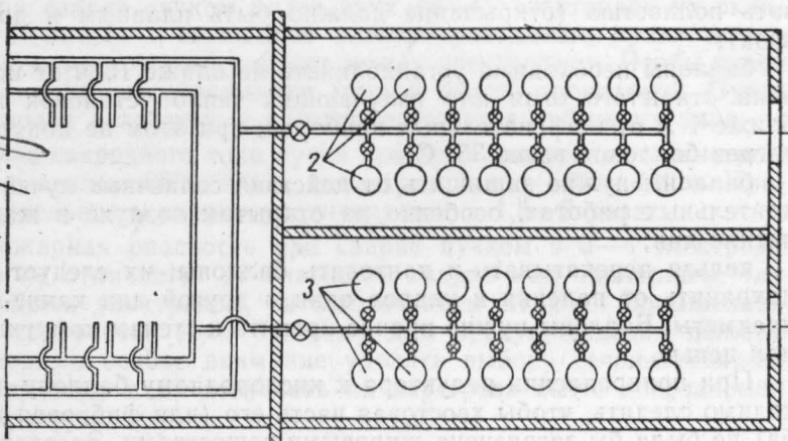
Схема расположения сварочной мастерской с подачей газов к постам от баллонов
